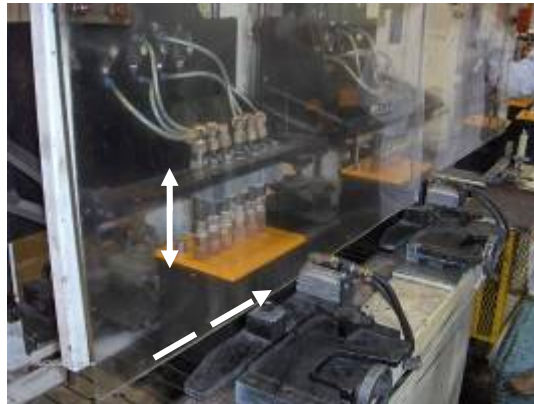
Prueba de fuga interna durante el proceso de ensamble
